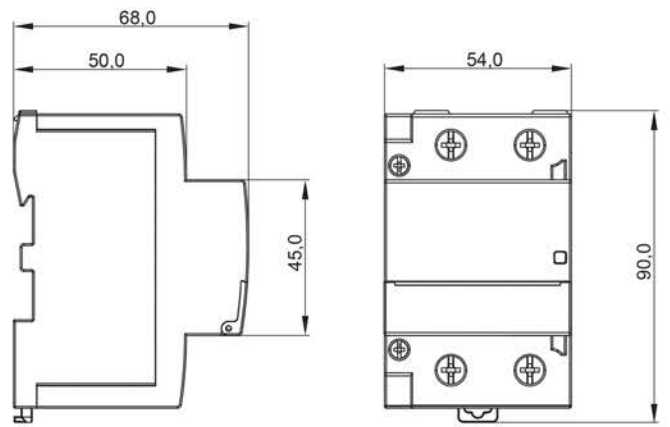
Габаритные размеры контакторов 100 А, 2P / Figure 5 – Overall dimensions of 100 A, 2P contactors
